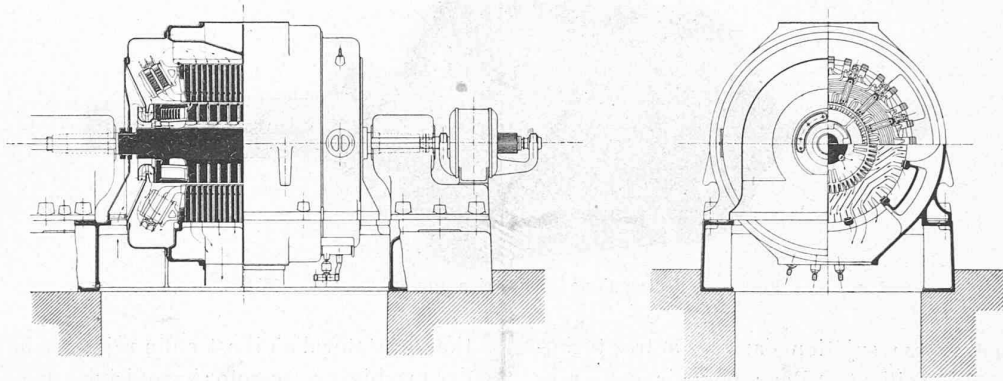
Turbo-alternateur à rotor cylindrique. Ventilation.
